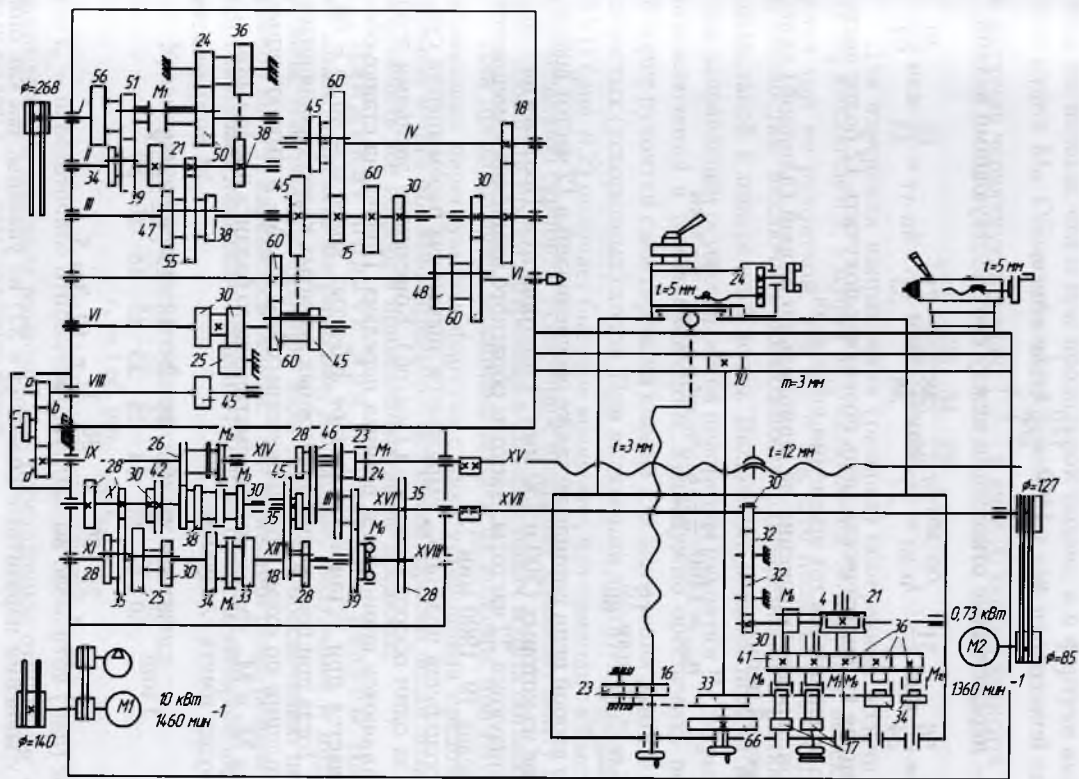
Кинематическая схема токарно-винторезного станка мод. 16К20
